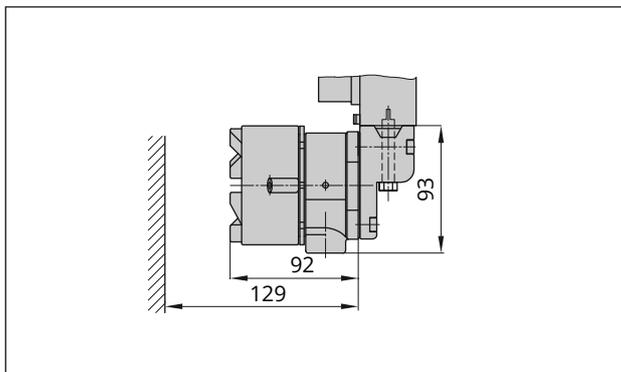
Maße in mm · Typ 6116-xx06011x000xxxx ohne Verstärkerteil mit Stellungsregler Typ 3766-000
